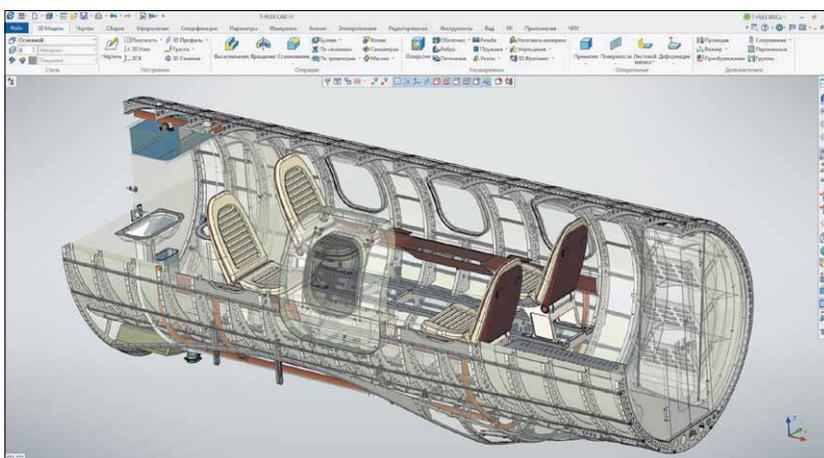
Пример сборочного компонента. Фюзеляж самолета в T-FLEX CAD
